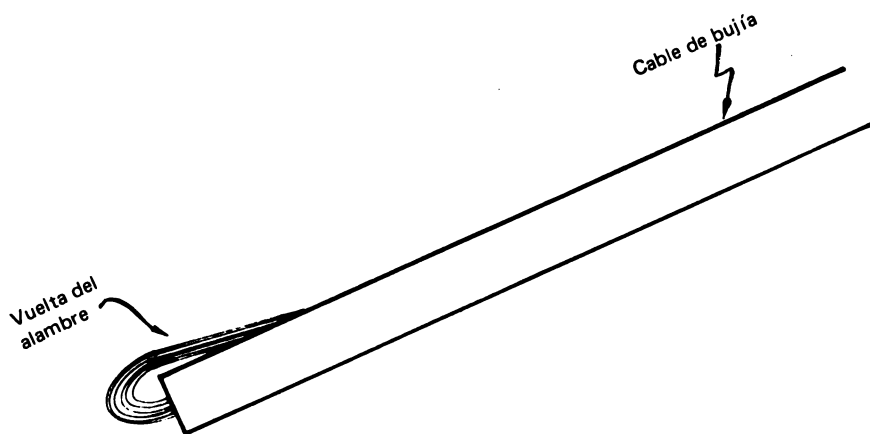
Para que el terminal de los cables de las bujías haga buen contacto se deja 1 cm de cable sin aislante.
